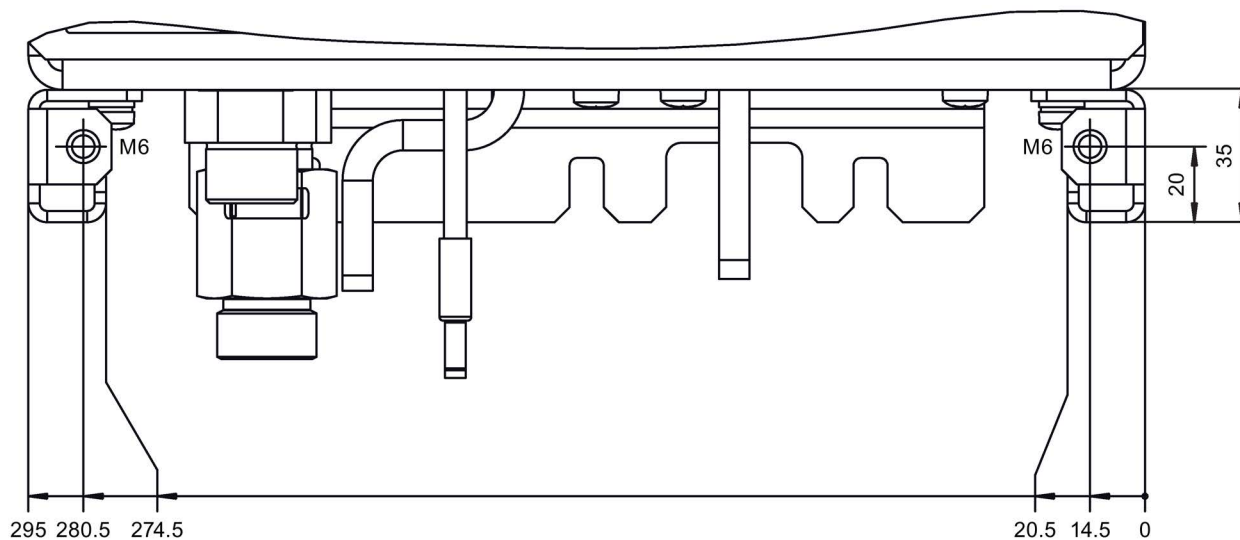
Профиль шины активного модуля питания и модуля двигателя, типоразмер JXL (размеры указаны в мм)
